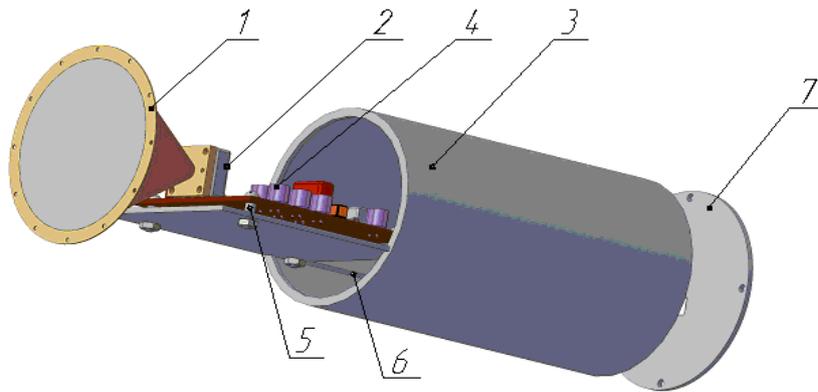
1 – антенное устройство; 2 – автодин; 3 – корпус; 4 – печатный узел; 5 – втулка дистанцирующая; 6 – фиксатор; 7 - крышка
